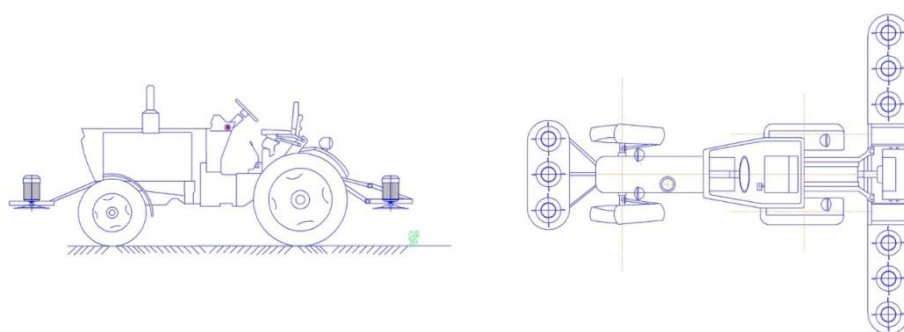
Схема предлагаемого агрегата СКБ-3,6 (главный вид, вид сверху)
